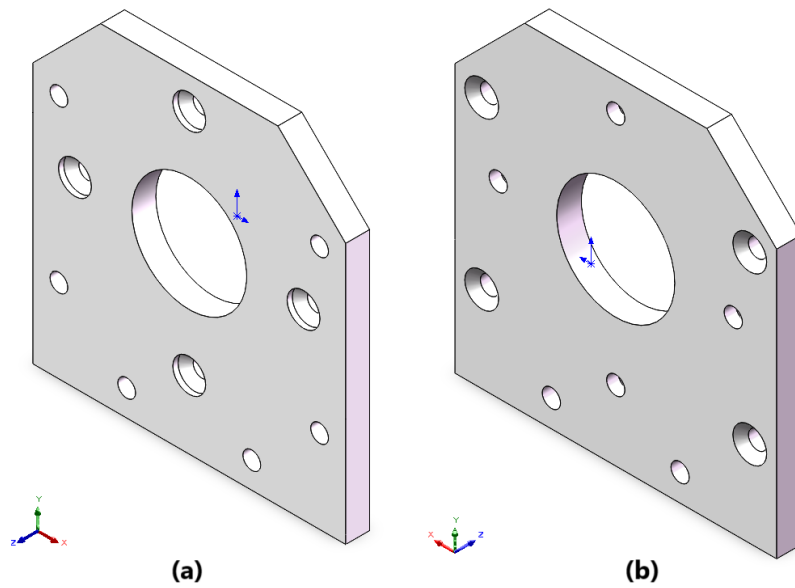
Espaçador do motor: a) face que estará em contacto com o outro espaçador; b) face que estará em contacto com o motor.
